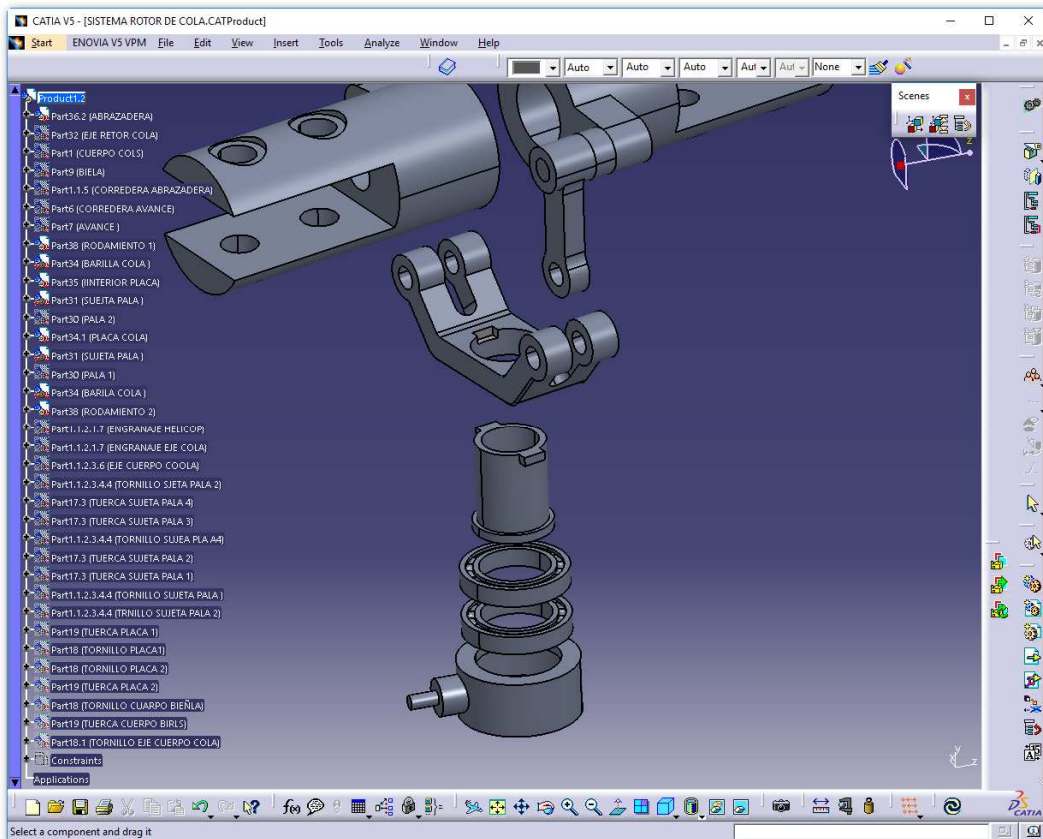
Montaje de placa – rodamientos – abrazadera.
